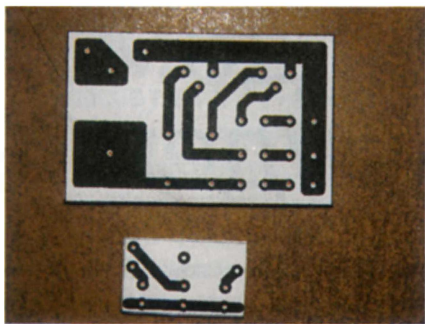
Печатная плата для сборки индикатора уровня напряжения.
